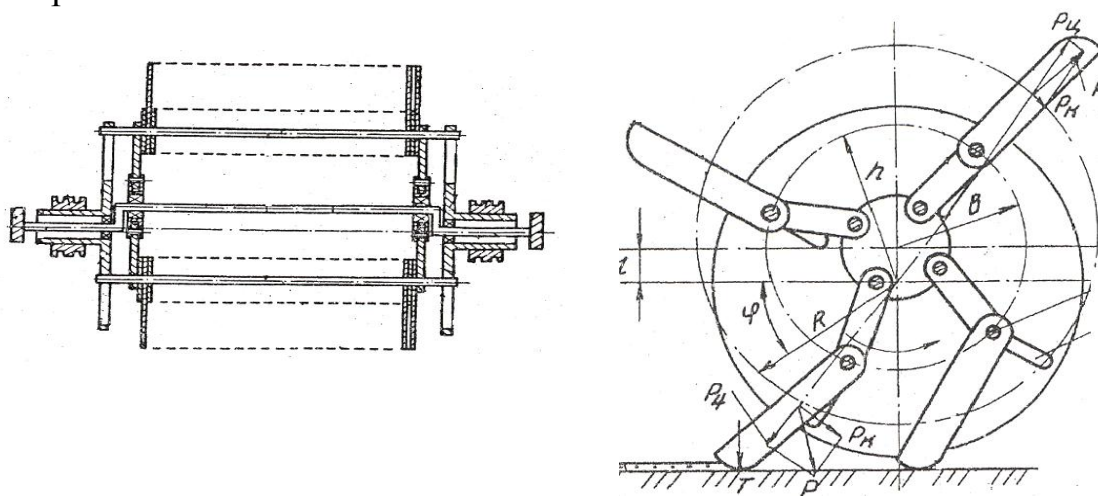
Схема рабочего оборудования (с эксцентрично расположенными тягами) для разрушения льда
